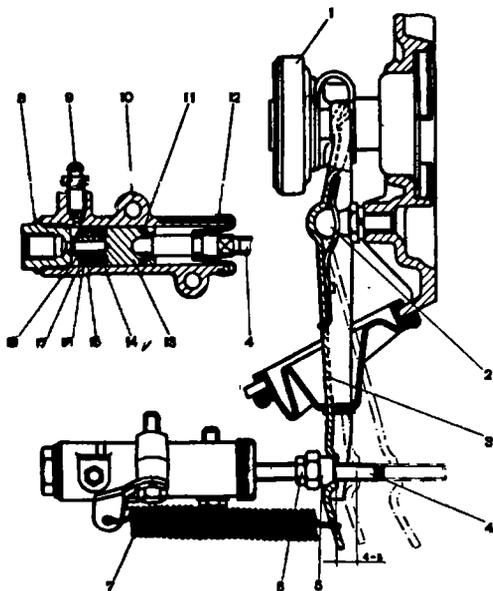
Рабочий цилиндр и вилка выключения сцепления: 1 - подшипник выключения сцепления; 2 - шаровая опора; 3 - вилка выключения сцепления; 4 - толкатель; 5 - регулировочная гайка; 6 - контргайка; 7 - оттяжная пружина; 8 - пробка корпуса; 9 - штуцер для прокачки; 10 - корпус цилиндра; 11 - уплотнительное кольцо; 12 - защитный колпачок; 13 - поршень; 14 - уплотнитель; 15 - тарелка; 16 - пружина; 17 - опорная шайба; 18 - стопорное кольцо
